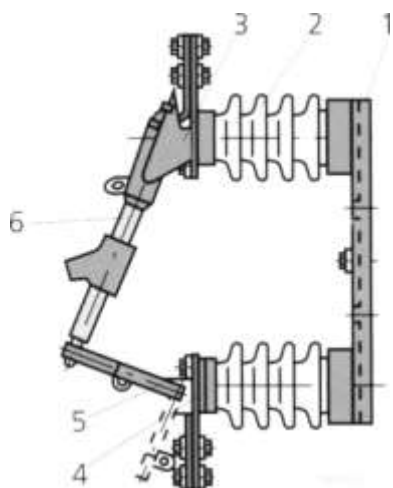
Газогенеруючий запобіжник ПСН - 35 на напругу 35 кВ і номінальний струм 40 А: 1 - основа; 2 - опорний ізолятор; 3 - верхня головка; 4 - нижня головка; 5 - контактний ніж; 6 - патрон.
